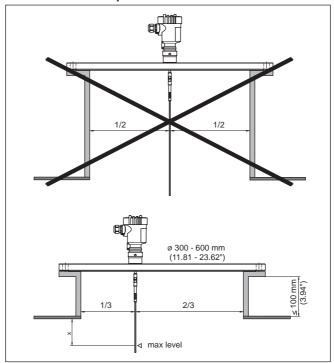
Montaje en una tubuladura de tanque ø 300 ... 600 mm (11.81 ... 23.62 in)
